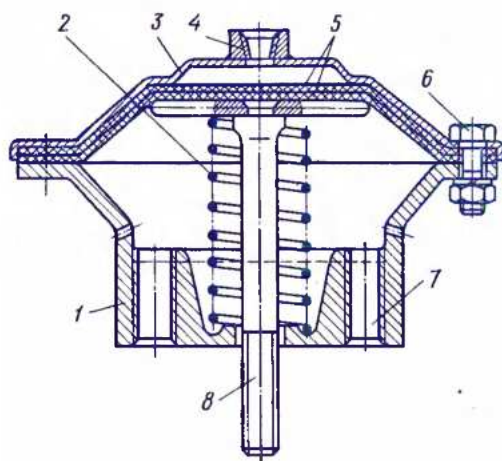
Пневматическая камера крана с пневмоуправлением:
